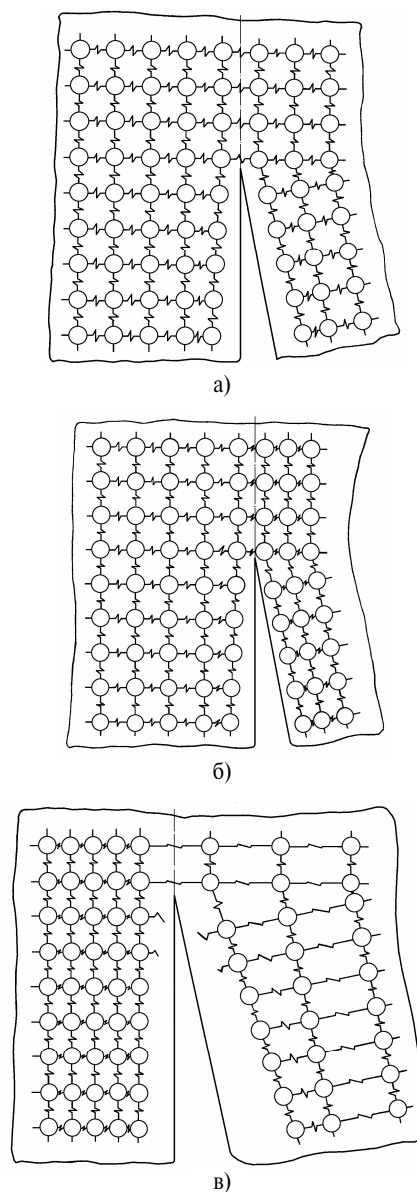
Динамическая атомная модель структуры сварного шва, поясняющая физическую природу источников зарождения непровара в процессе сварки
